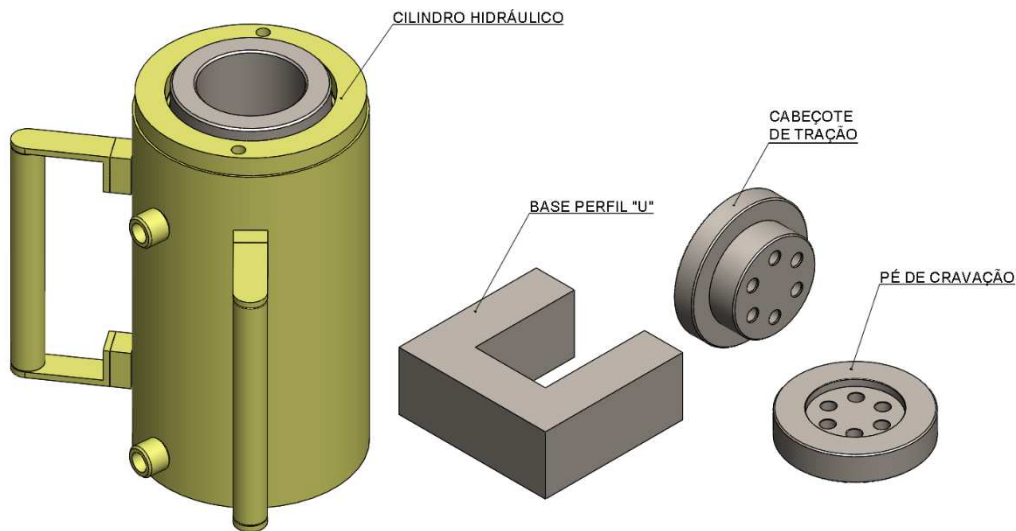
Ilustração com os principais componentes do conjunto de protensão
